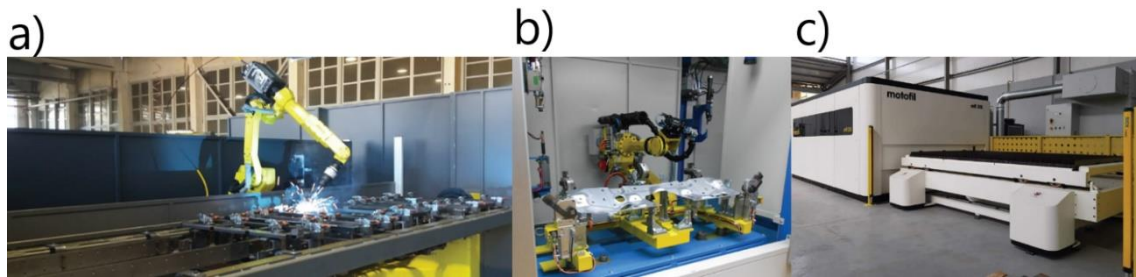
Produtos: a) soldadura b) manipulação c) corte laser
